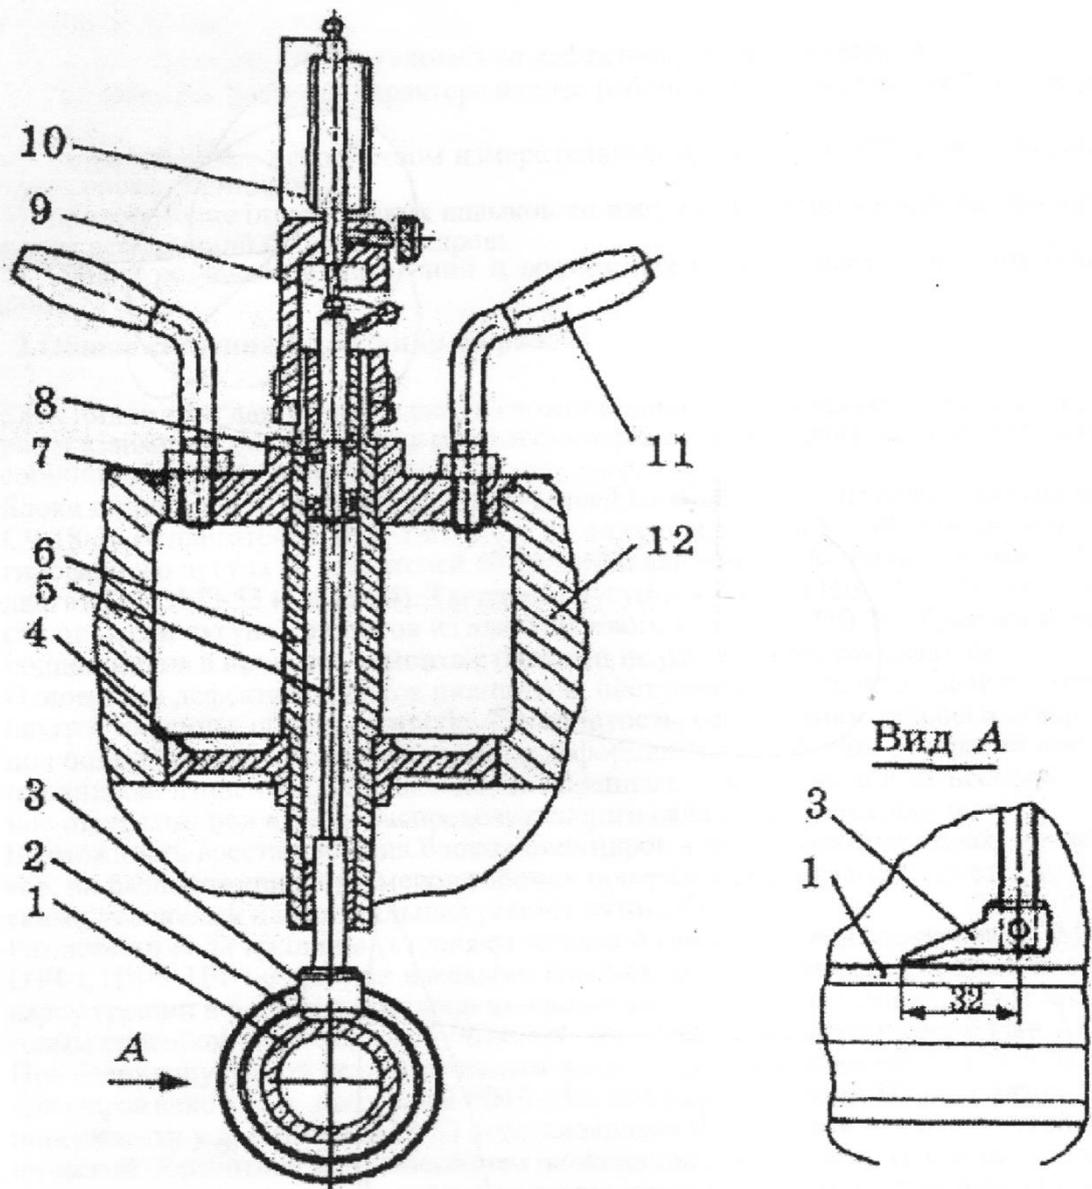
Приспособление для проверки перпендикулярности оси цилиндра к оси коленчатого вала двигателя:
